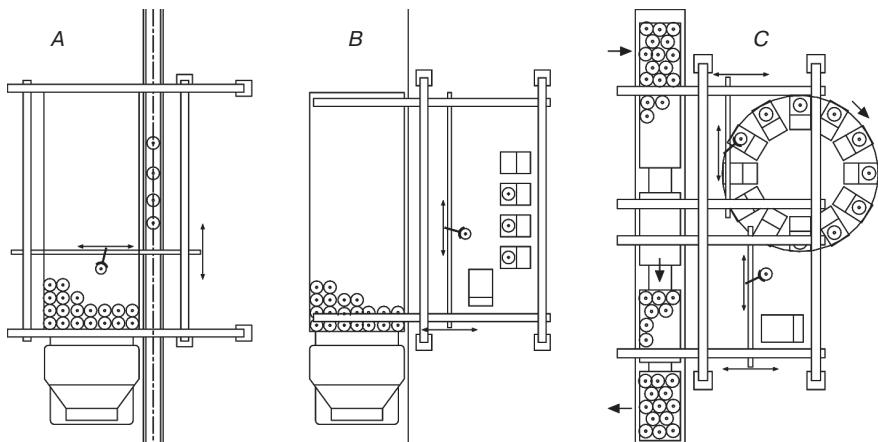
Погрузка/выгрузка отдельных баллонов с помощью подвесной рельсовой системы:
